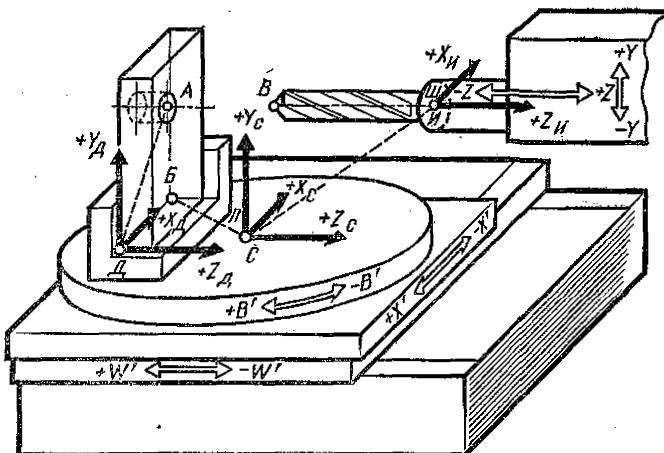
Связь систем координат детали, станка и инструмента при обработке на сверлильно-расточном станке
